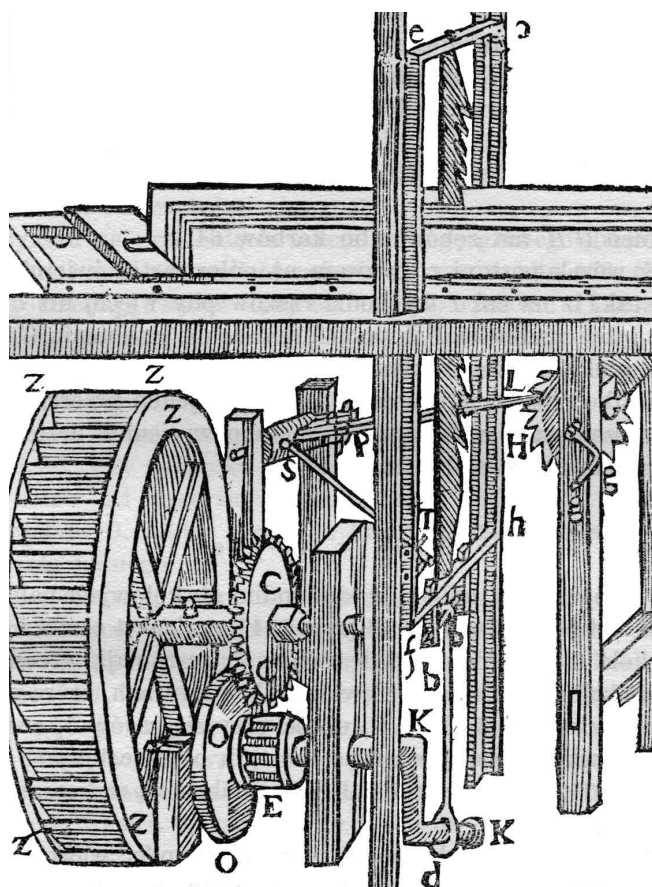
Pilarki ramowe konstrukcji Jacopo Strady (STRADA 1617-1618)
